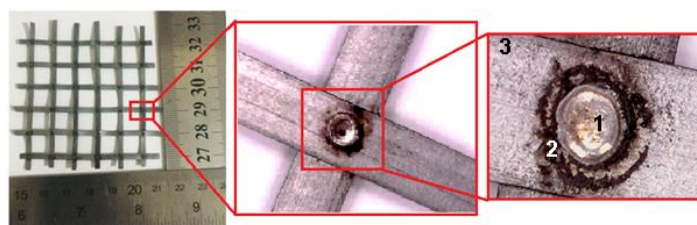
Malha soldada de LMF Ni-Ti com detalhes do ponto de solda TIG.
